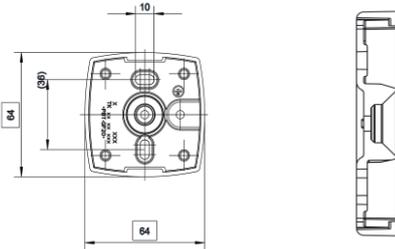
Draufsicht und Querschnitt der Adapterplatte
